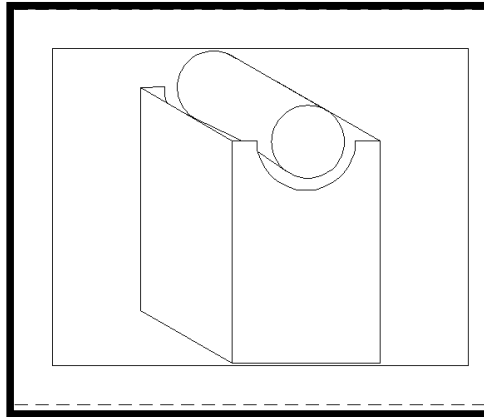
Dispositivo de apoyo para ensayo a flexión del bambú.
